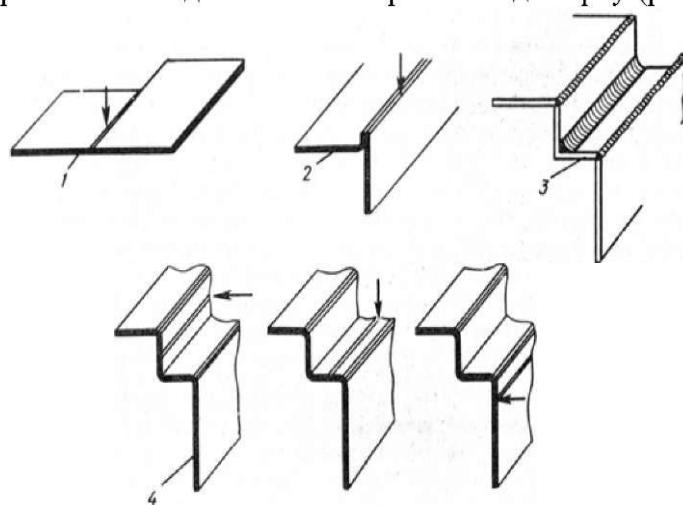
Подготовка кромок тонких листов под сварку: 1 - сварка встык; 2 - сварка с отбортовкой кромки; 3 - сварка внутренних или наружных углов не подвергается рихтовке; 4 - хорошее расположение сварочного шва, позволяющего производить рихтовку
